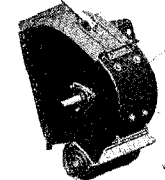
Домолачивающее устройство: 1 – крышка; 2 – опора
